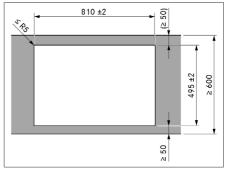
Dimensioni intaglio per montaggio in battuta
